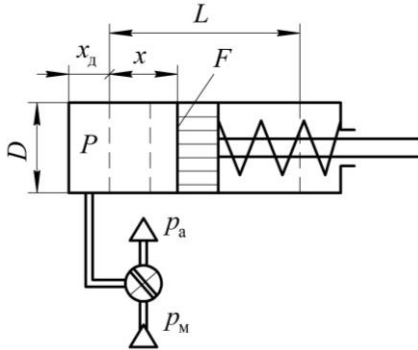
Розрахункова схема одностороннього пневмопривода зі зворотною пружиною
